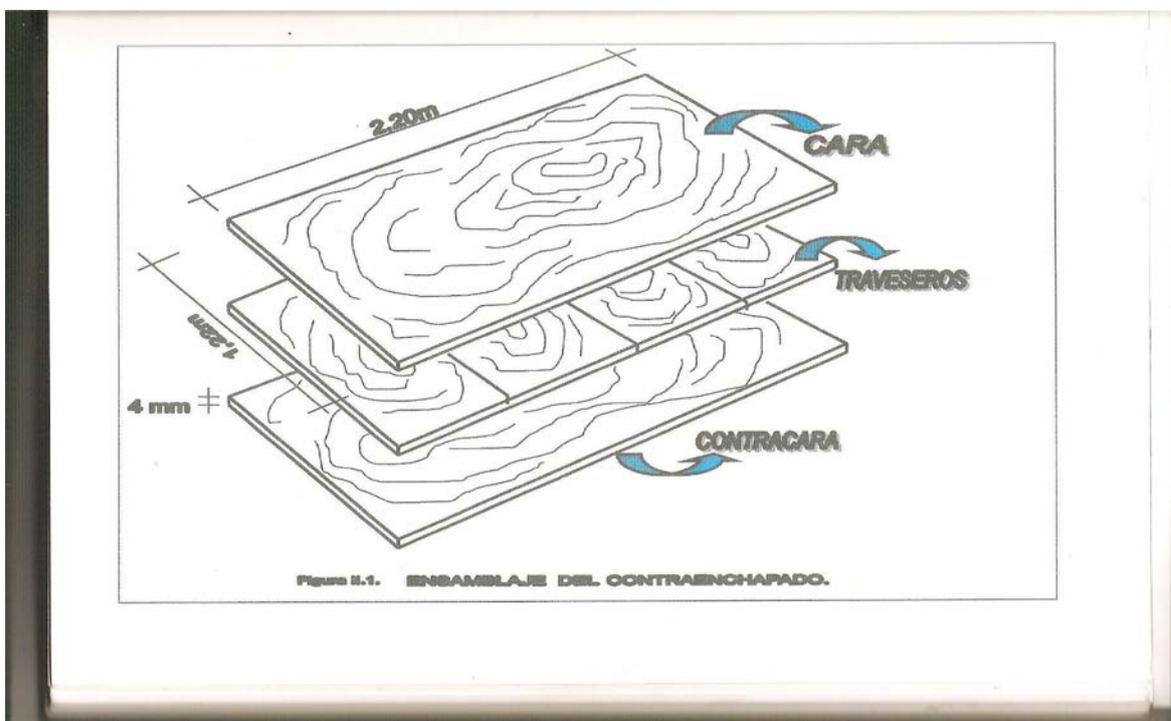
Ensamblaje de la lámina de contrachapado (Elaboración propia)
